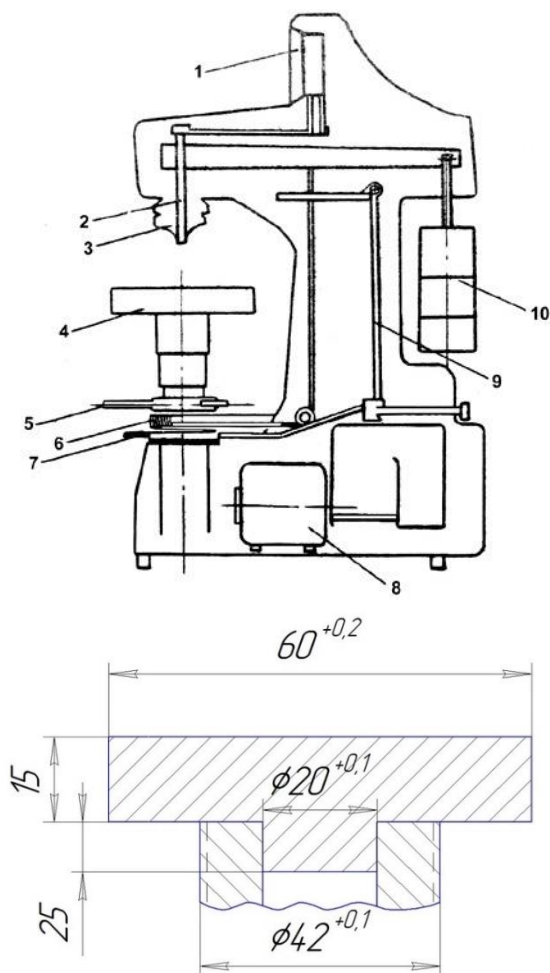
Схема прибора типа ТК-2М и столика для установки изделия для измерения твердости вдавливанием алмазного конуса или стального шарика по методу Роквелла: 1 – шкала индикатора; 2 – щиток с алмазным конусом, шариком; 3 – чехол для индикатора; 4 – столик для установки образца; 5 – маховик; 6 – кольцо для перемещения шкалы индикатора; 7 – пусковая педаль; 8 – электромотор; 9 – шток, управляющий работой механизма нагружения; 10 – груз.
